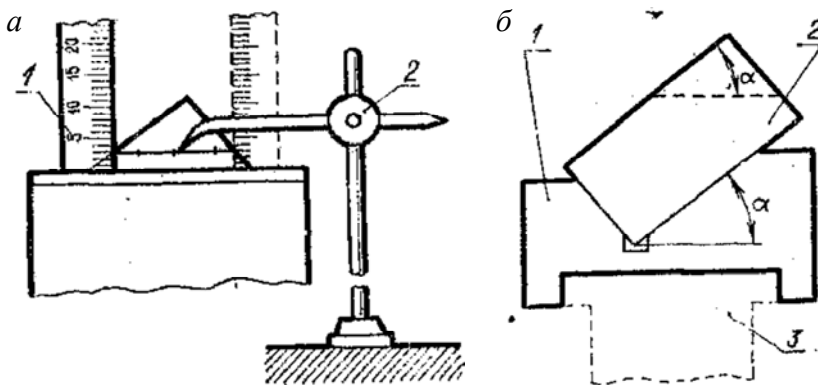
Поворот заготовки при фрезеровании наклонных поверхностей:
